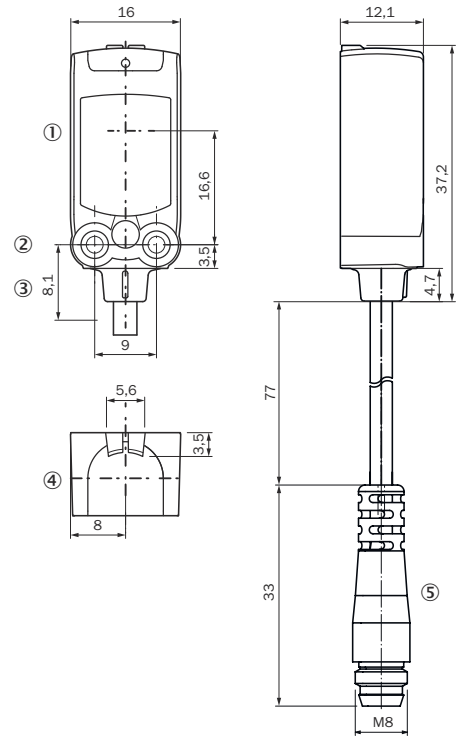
Maßzeichnung 2, Leitung mit Stecker M8
